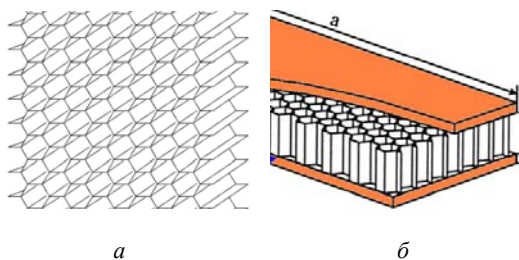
а – типичный вид элемента сотовой конструкции (Fig. 2. Technical honeycomb terminology [1]); б – фрагмент сотовой панели типа «сэндвич» (Fig. 2. Honeycomb sandwich plate [2]).
